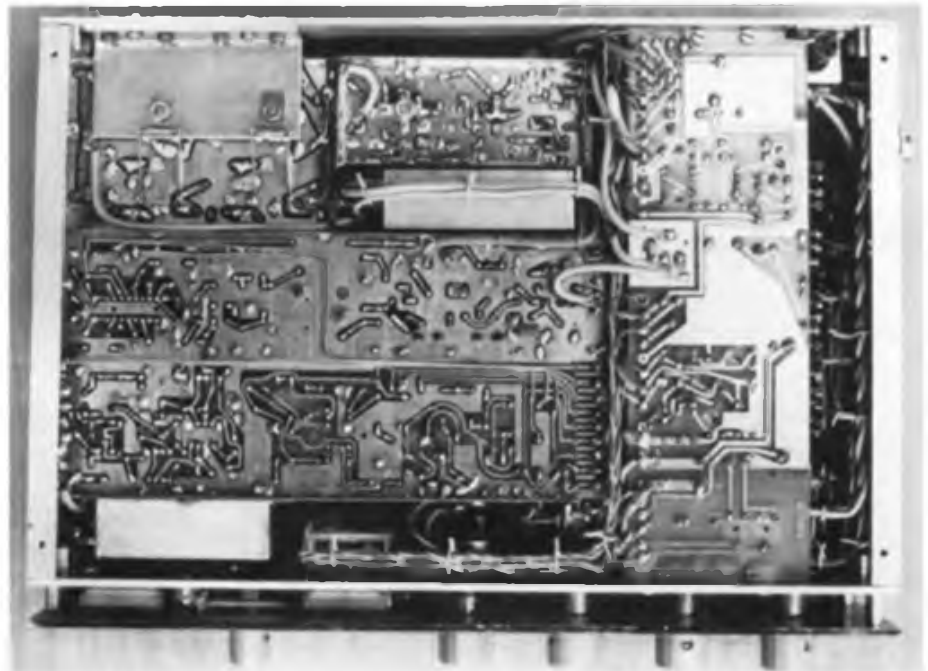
Ansicht des geöffneten Geräts von unten. Links oben im Bild Sendeend- und -vorverstärker sowie Stehwellenmesser [3], darunter die Empfängerbaugruppe [4], rechts die Systemleiterplatte
